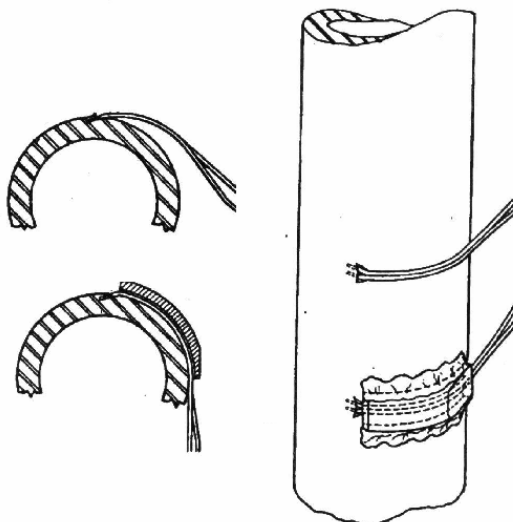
Método de fixar os termoelementos na superfície externa de tubos.
